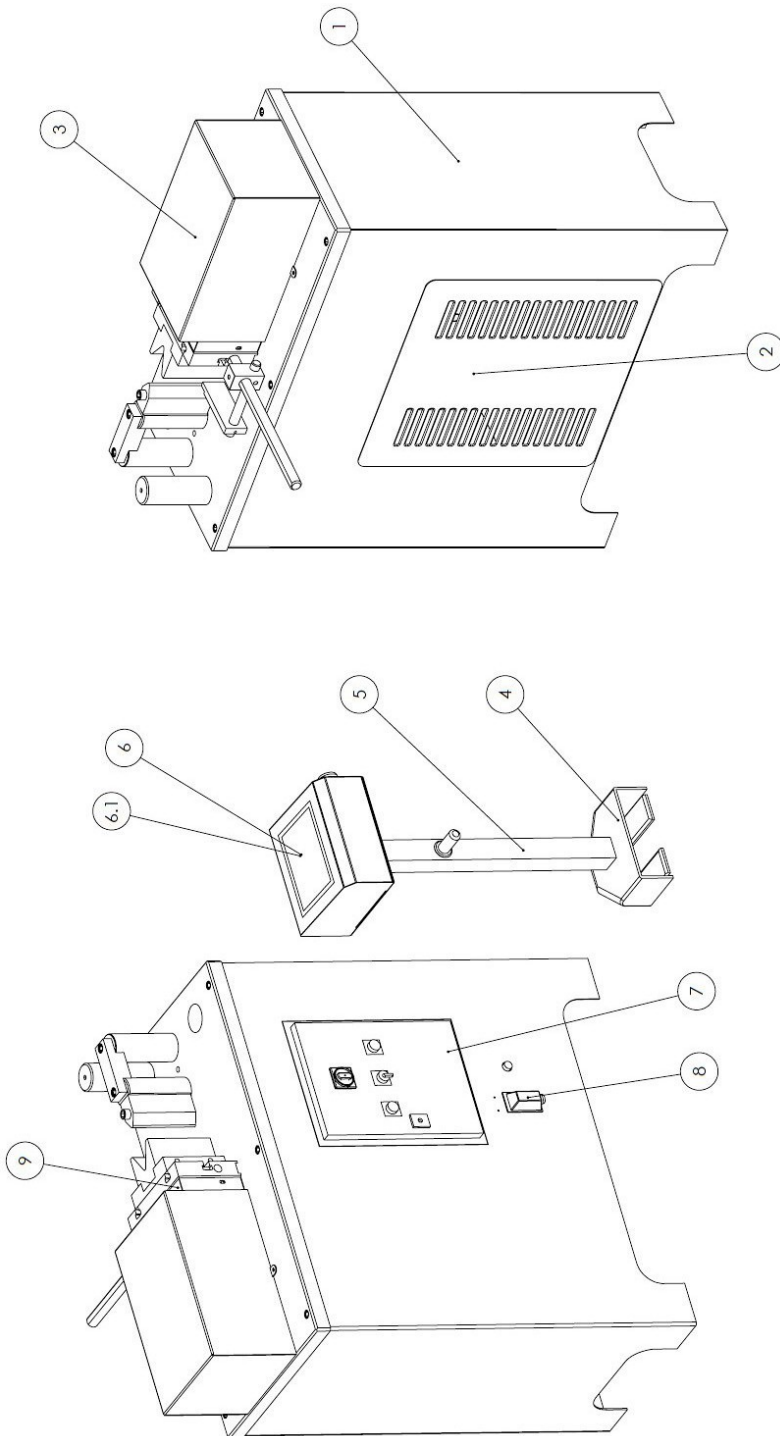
Schéma des pièces 1 Machine complète HBP 10
